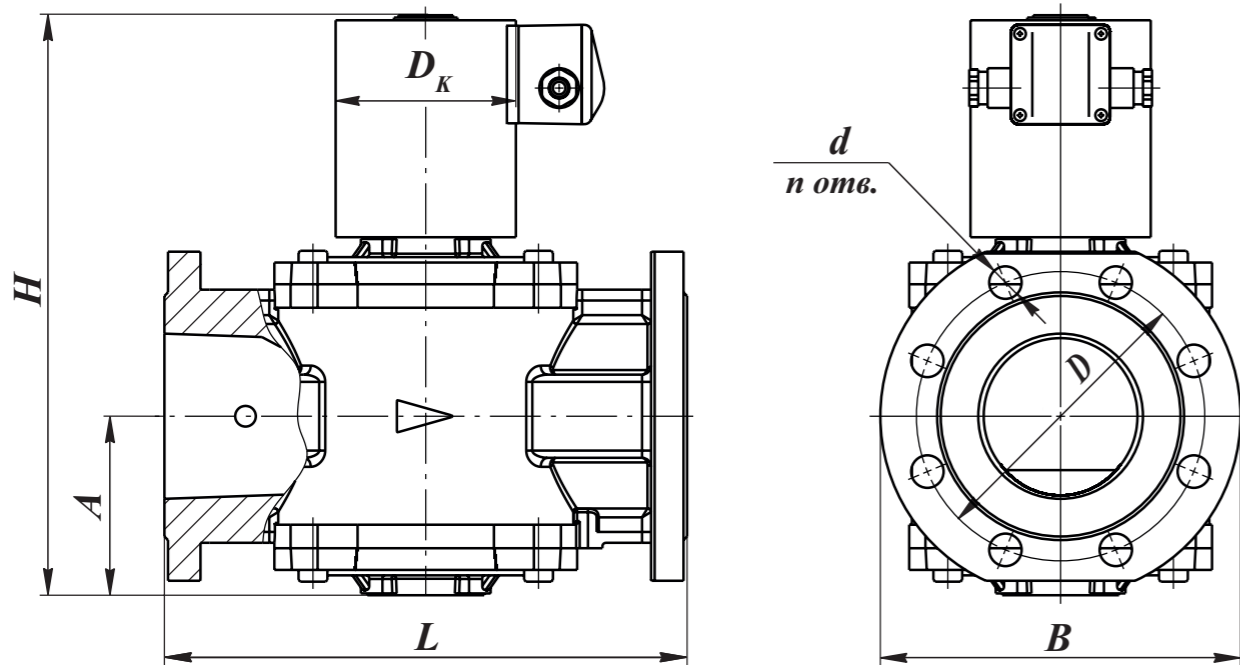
Клапаны на DN 50 - 100 фланцевые нормально-открытые (исполнение: с присоединительными фланцами PN16)
